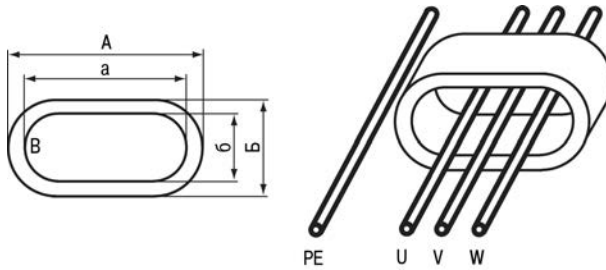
Внешний вид и установка ФРПх на кабель
